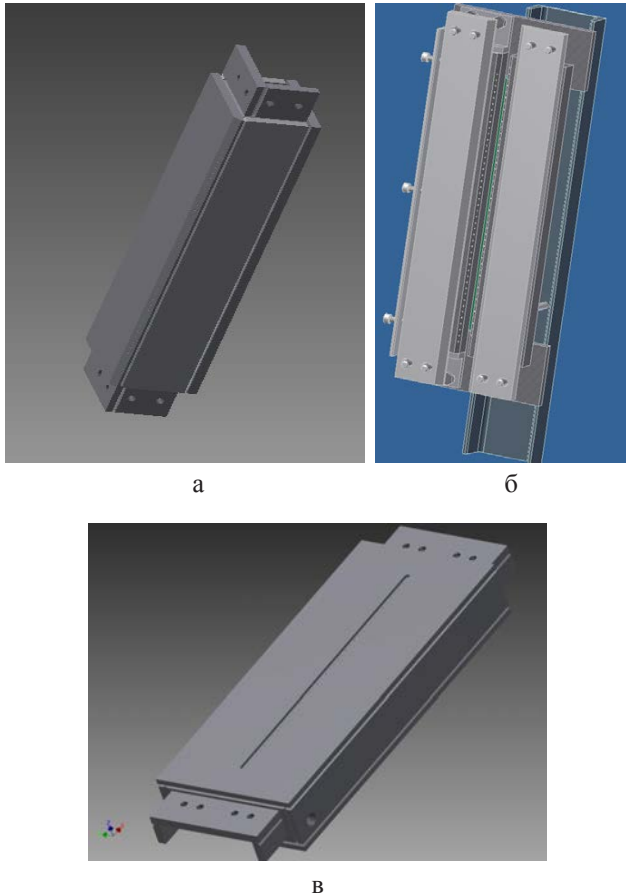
Модель струбцини для зварювання контрольних зварних з'єднань: а – кутових; б – таврових; в – стикових і напусткових
